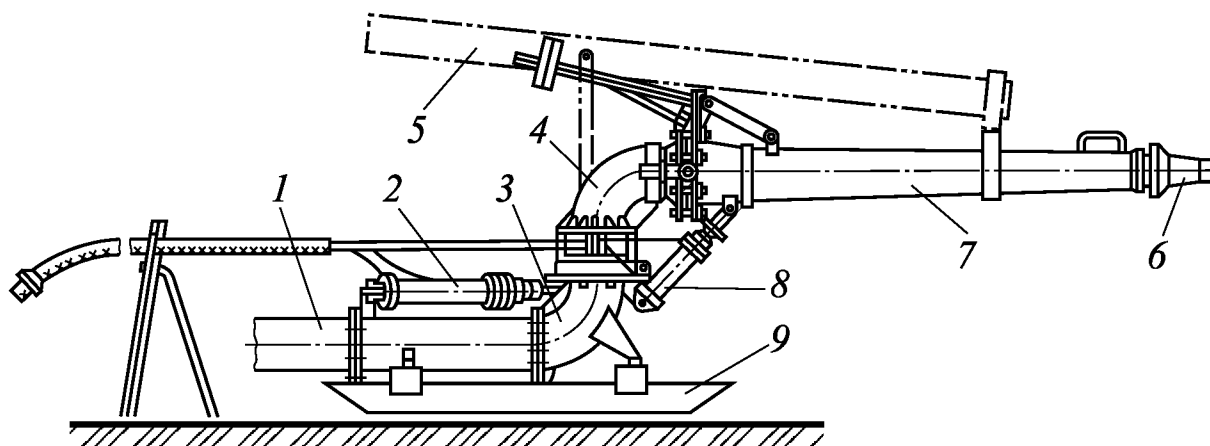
Гидромонитор: 1 – напорный трубопровод; 2, 8 – гидроцилиндры; 3 – нижний неподвижный трубопровод; 4 – верхнее колено; 5 – рычаг; 6 – насадка; 7 – ствол; 9 – салазки
